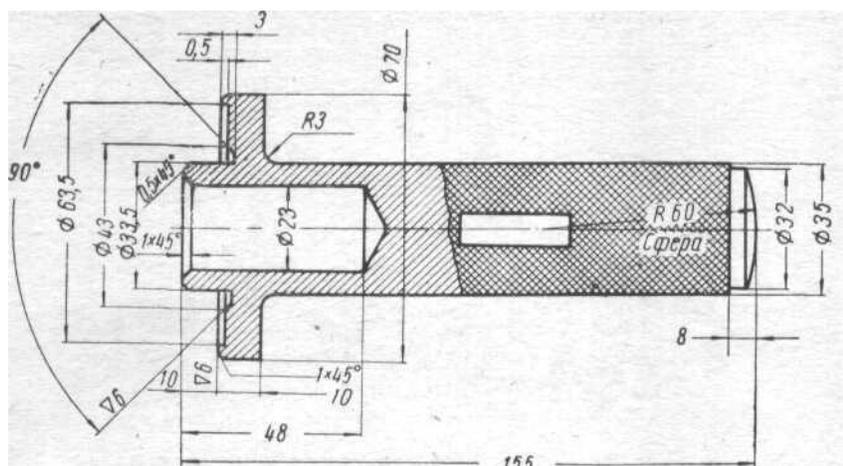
Оправка для запрессовывания сальника в горловину картера редуктора
